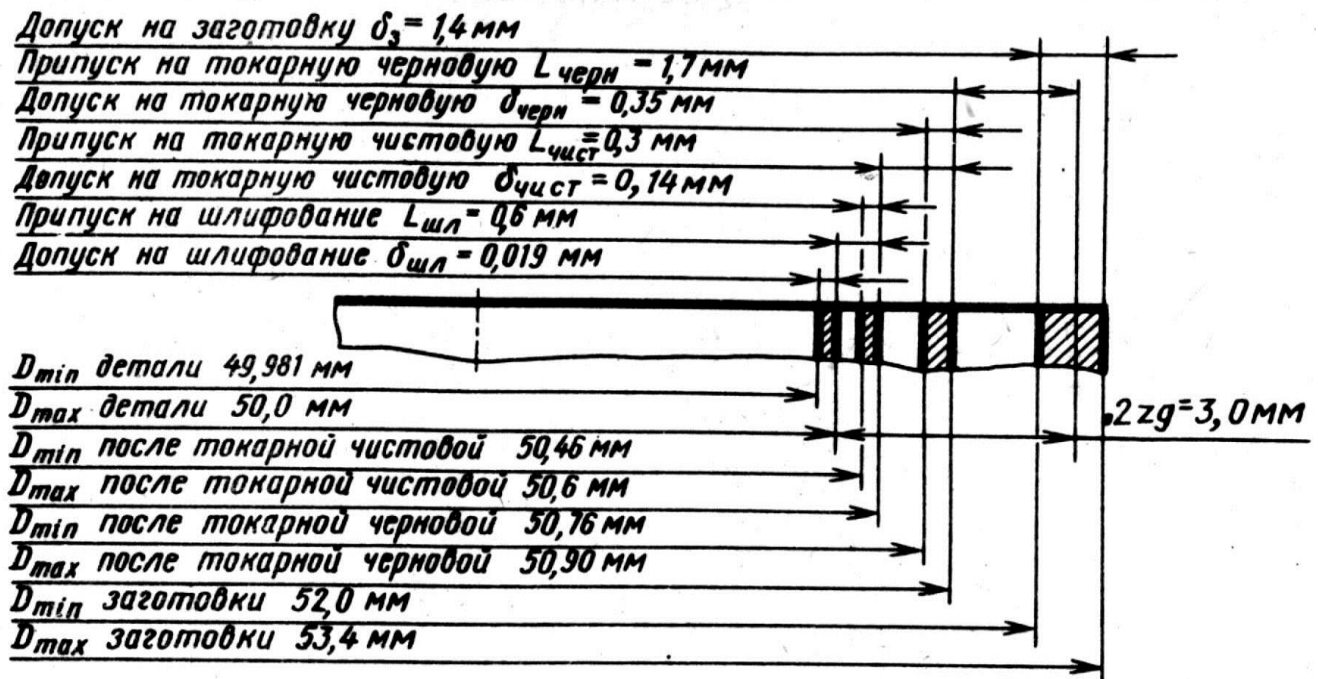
Пример расположения полей допусков и промежуточных размеров для операций
